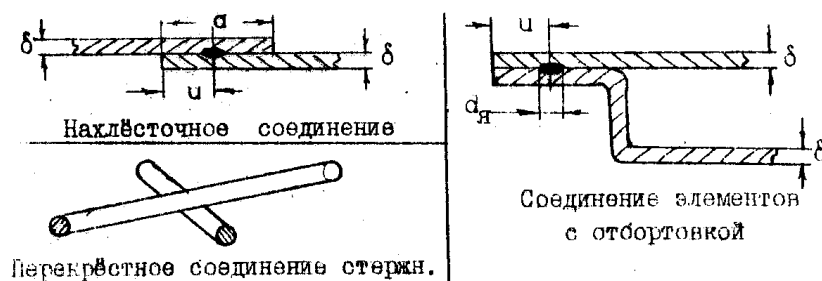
Некоторые типы сварных соединений при точечной контактной сварке
